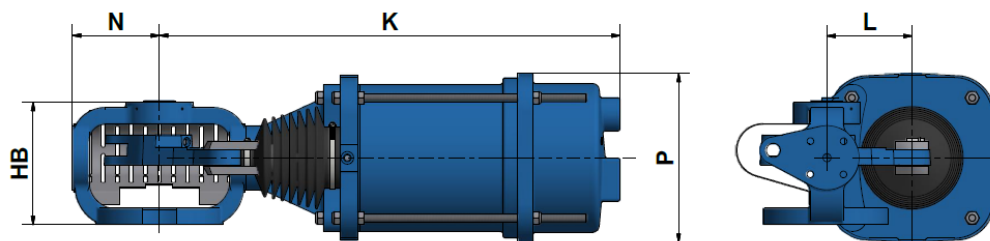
Maßzeichnung für Antriebe Typ R mit VETEC-Bügel
